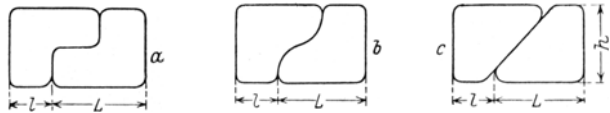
Formen der Steuerschlitzze für Einschieber-Steuerungen.
